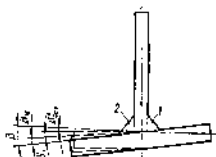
Элементы угловой деформации при сварке шва от второго углового шва
